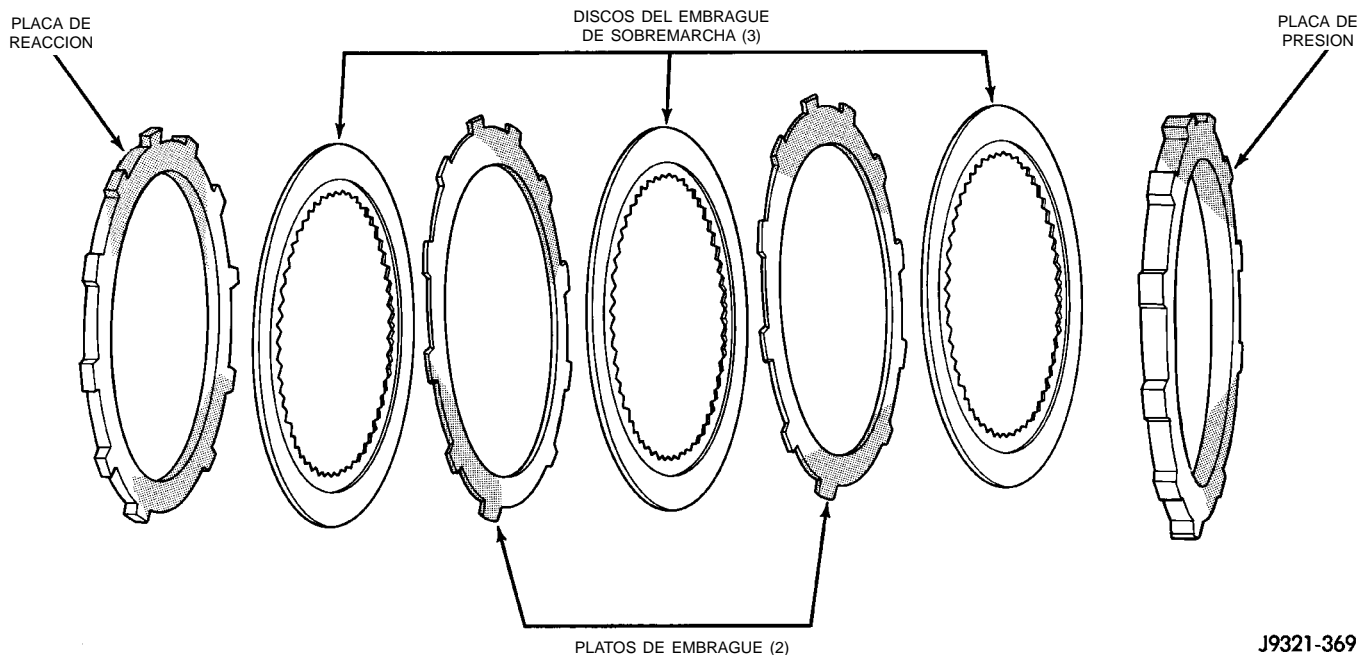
Componentes del embrague de sobremarcha de la 42RE
